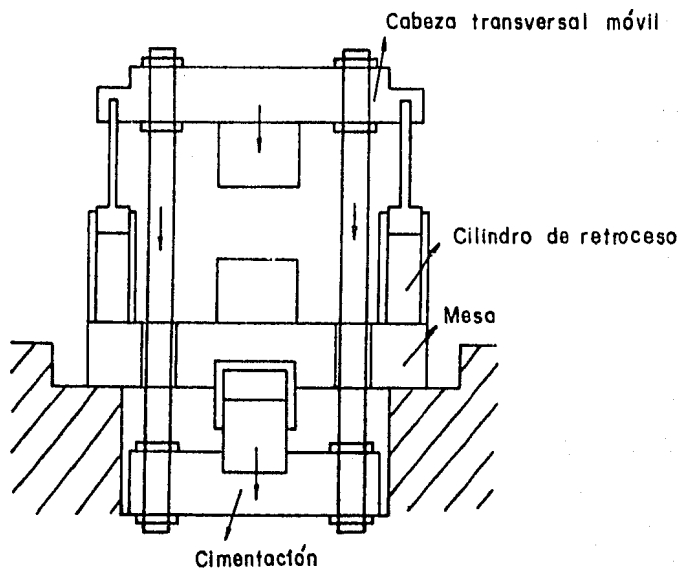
b CONJUNTO BASTIDOR-CILINDRO MOVIL
